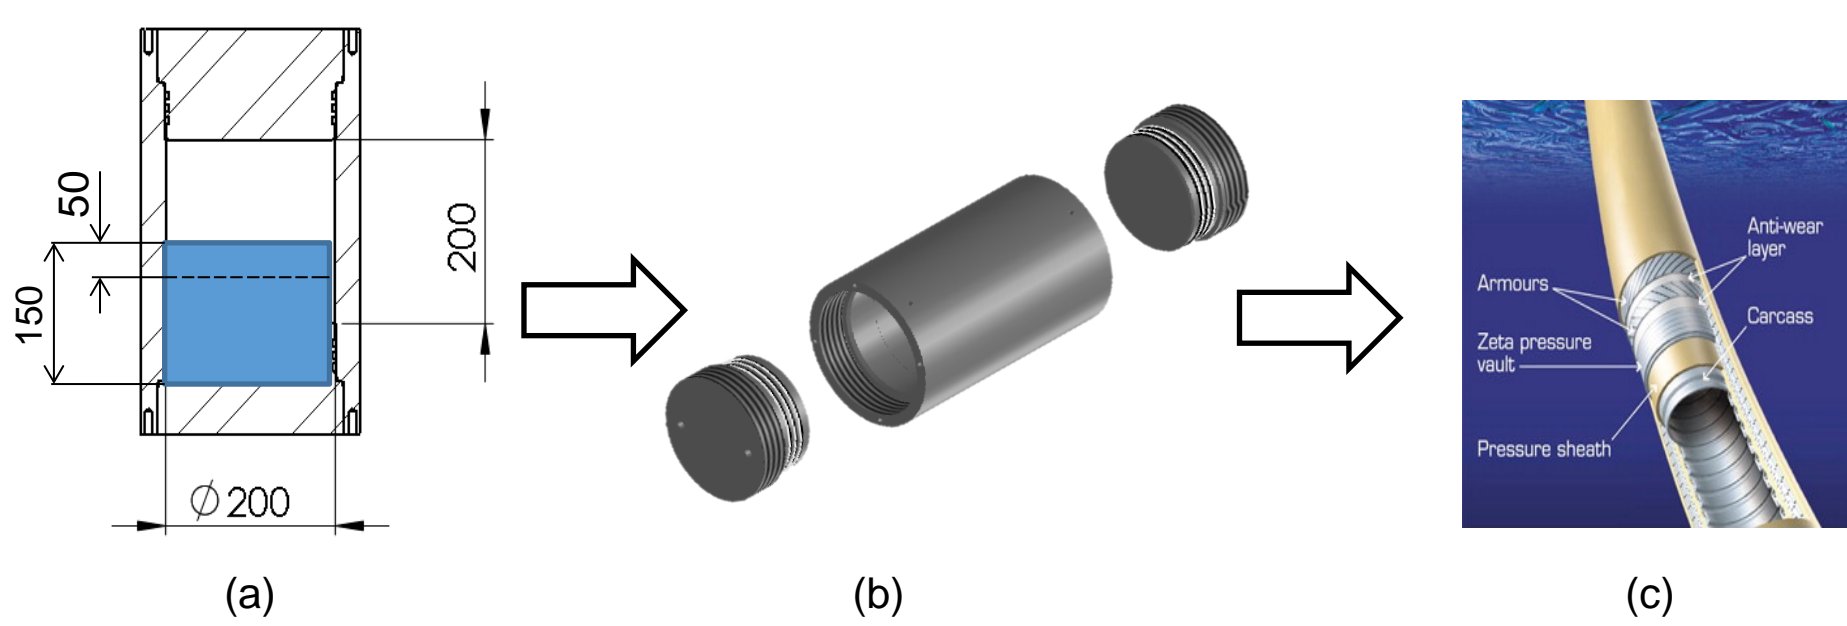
a) Desenho técnico do vaso de pressão com principais dimensões especificadas – diâmetro interno, altura interna, área com resina e área com desmoldante; b) Representação do equipamento em CAD; c) Camadas internas de um riser flexível;
